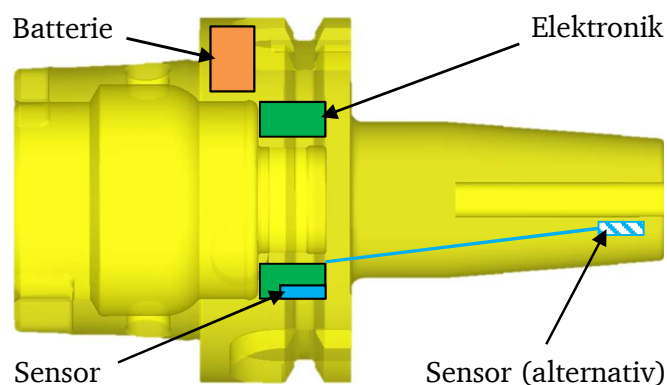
Einbauraum in einer Werkzeugaufnahme mit HSK-Schnittstelle
